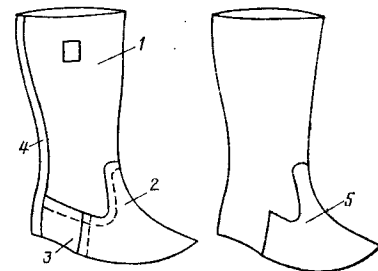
Детали верха сапог с голенищами из обувной кирзы:
